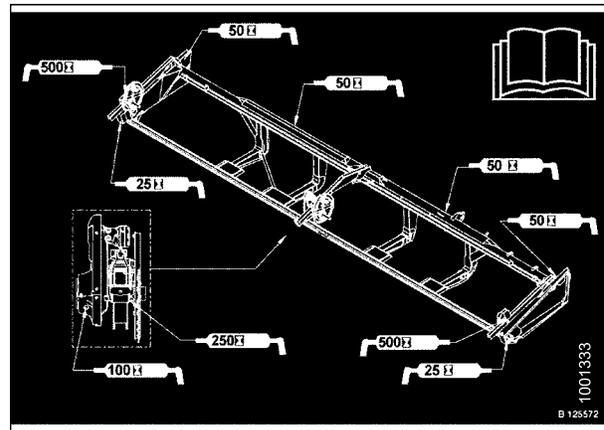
Наклейка с основными точками смазки на жатке с двойным ножом
